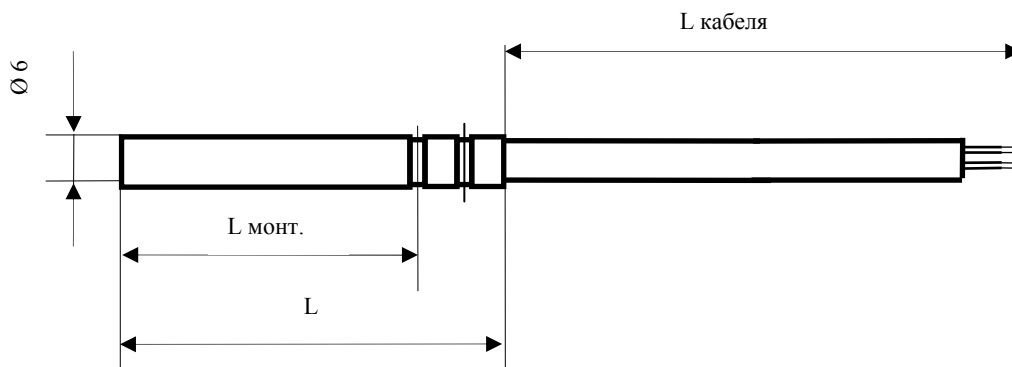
Габаритные и присоединительные размеры ТСП 001-01
